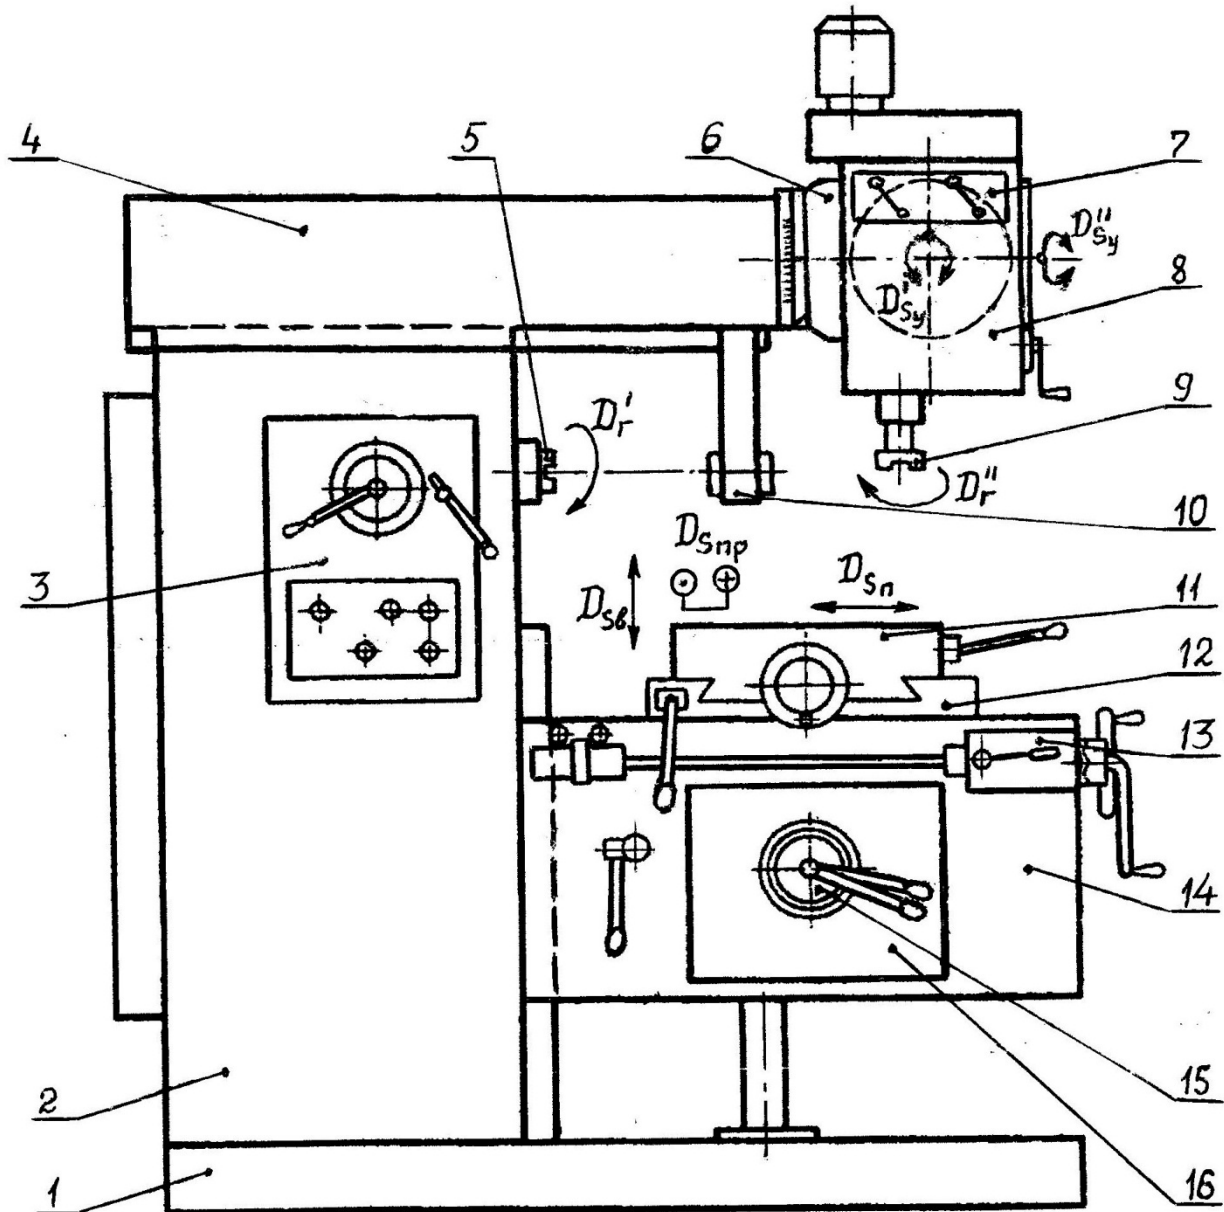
Схема компонентов широкоуниверсального консольно-фрезерного станка: 1 – фундаментная плита с емкостью для СОЖ; 2 – станина (стойка) с направляющими горизонтальными для перемещения ползуна и вертикальными для перемещения консоли; 3 – коробка скоростей с приводом, кнопочной станцией и рукоятками переключения частот вращения горизонтального шпинделя; 4 – ползун (хобот); 5 – горизонтальный шпиндель; 6 – кронштейн в виде угольника для размещения вертикальной фрезерной головки; 7 – коробка скоростей фрезерной головки с приводом и механизмом переключения частот вращения вертикального шпинделя; 8 – вертикальная поворотная фрезерная головка; 9 – вертикальный шпиндель; 10 – съемная подвеска (серьга) для размещения конца установленной в горизонтальный шпиндель центровкой оправки;
